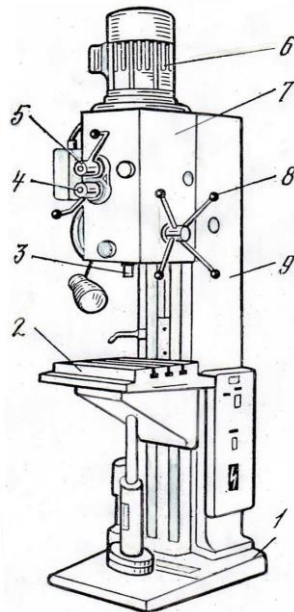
Вертикально-сверлильный станок мод. 2Н118
